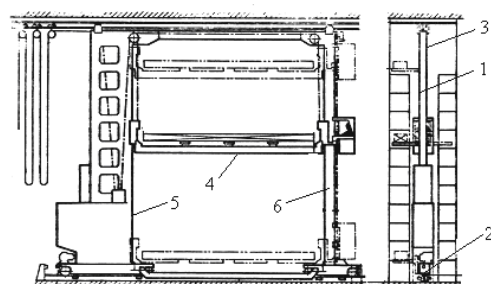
Схема стеллажного двухколонного крана-штабелера, опирающегося на напольный рельс
